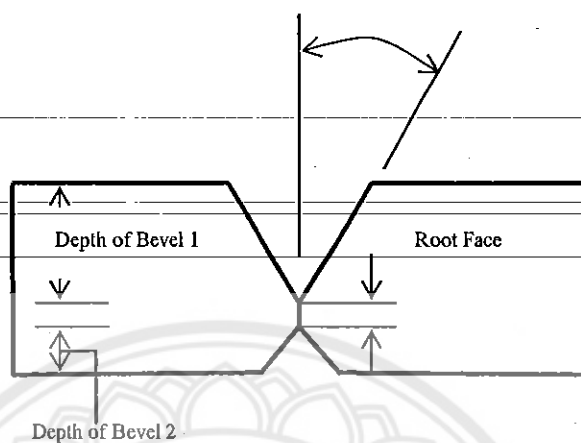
แสดง Single V Single Side Weld [2]
